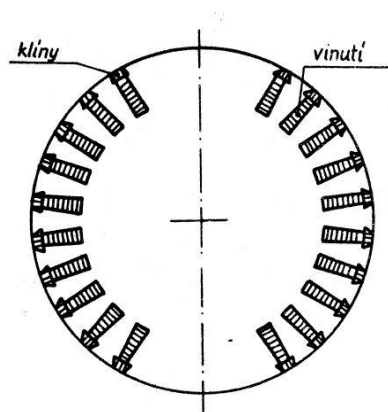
Stator a rotor hydroalternátoru (VE Štěchovice)
